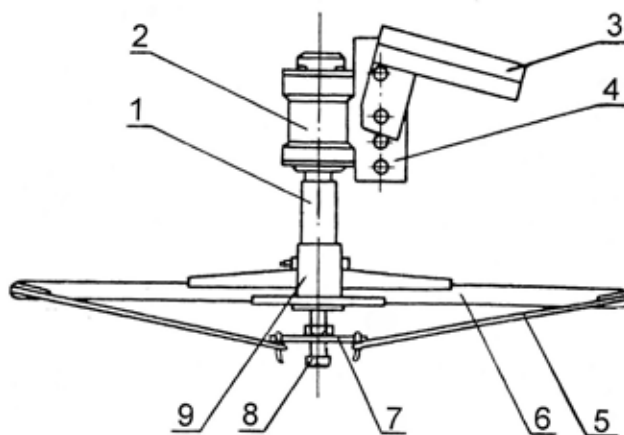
Пальцевой ротационный рабочий орган ПРО: 1 — ось; 2 — корпус подшипников; 3 — держатель квадратного сечения; 4 — кронштейн; 5 — проволока; 6 — стальные пальцы; 7 — регулировочный диск; 8 — винт; 9 — ступица.
